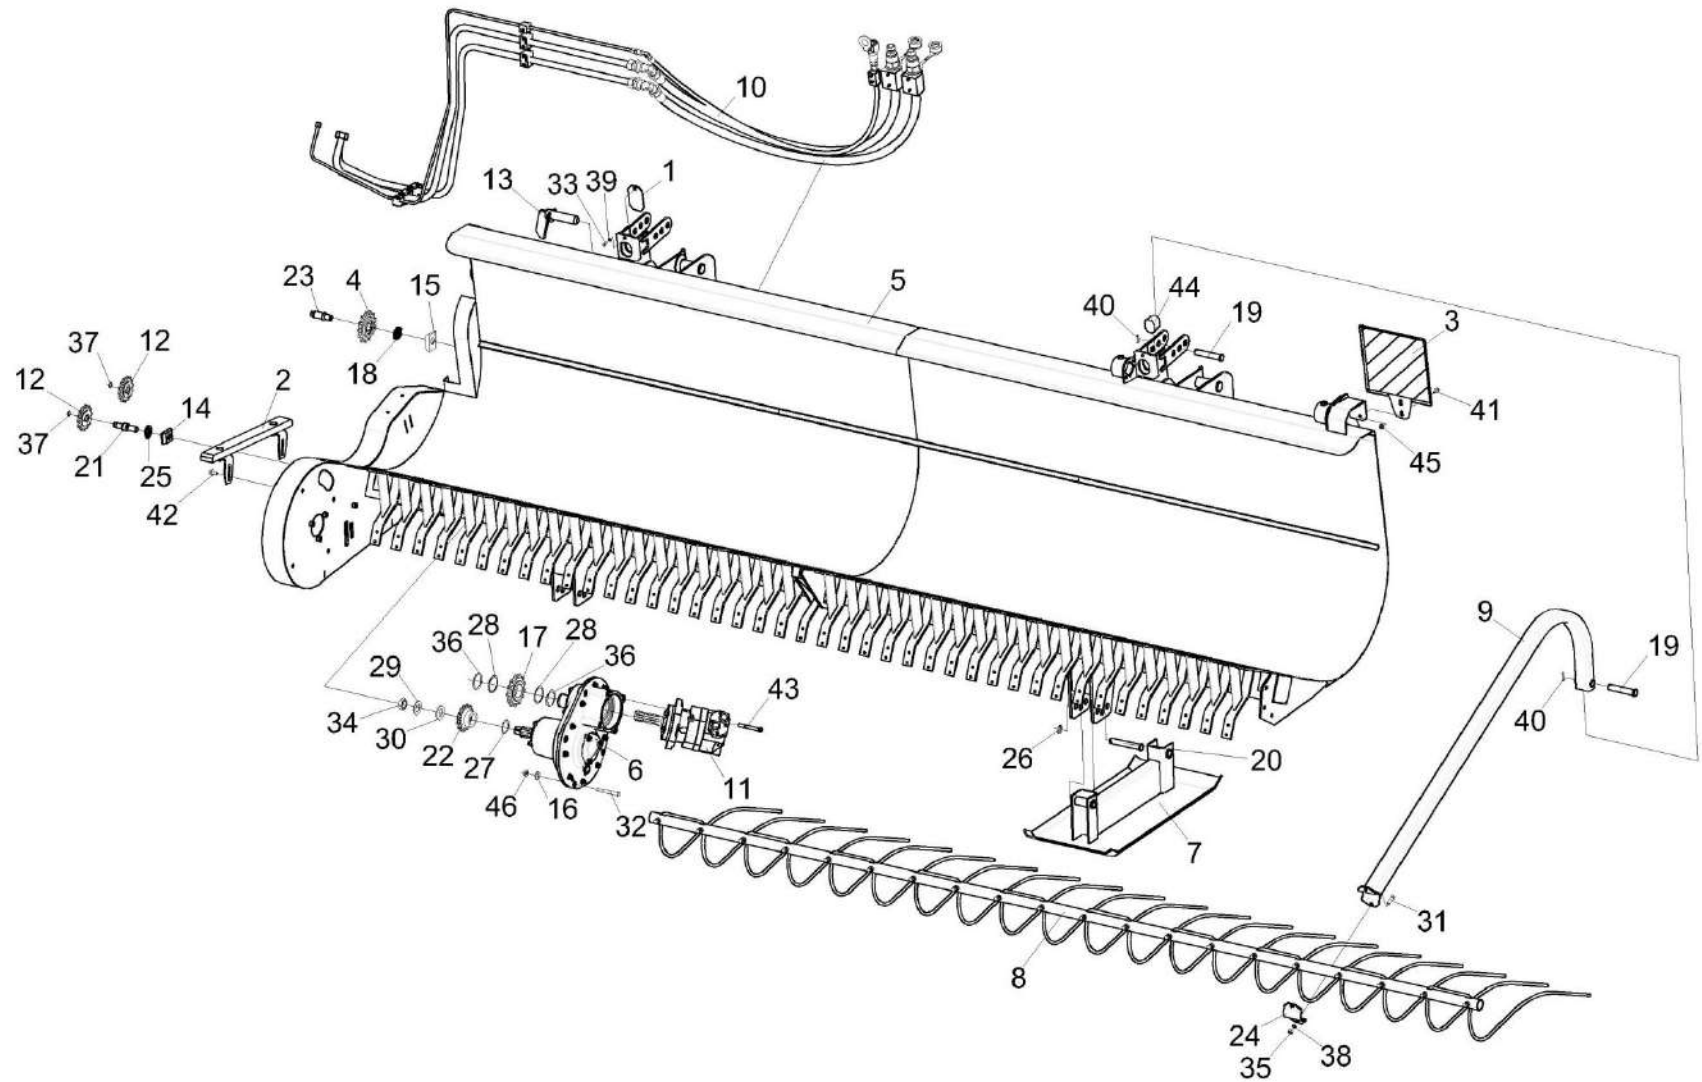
Валкооборачиватель КС-100-4900000 (лист 2)
